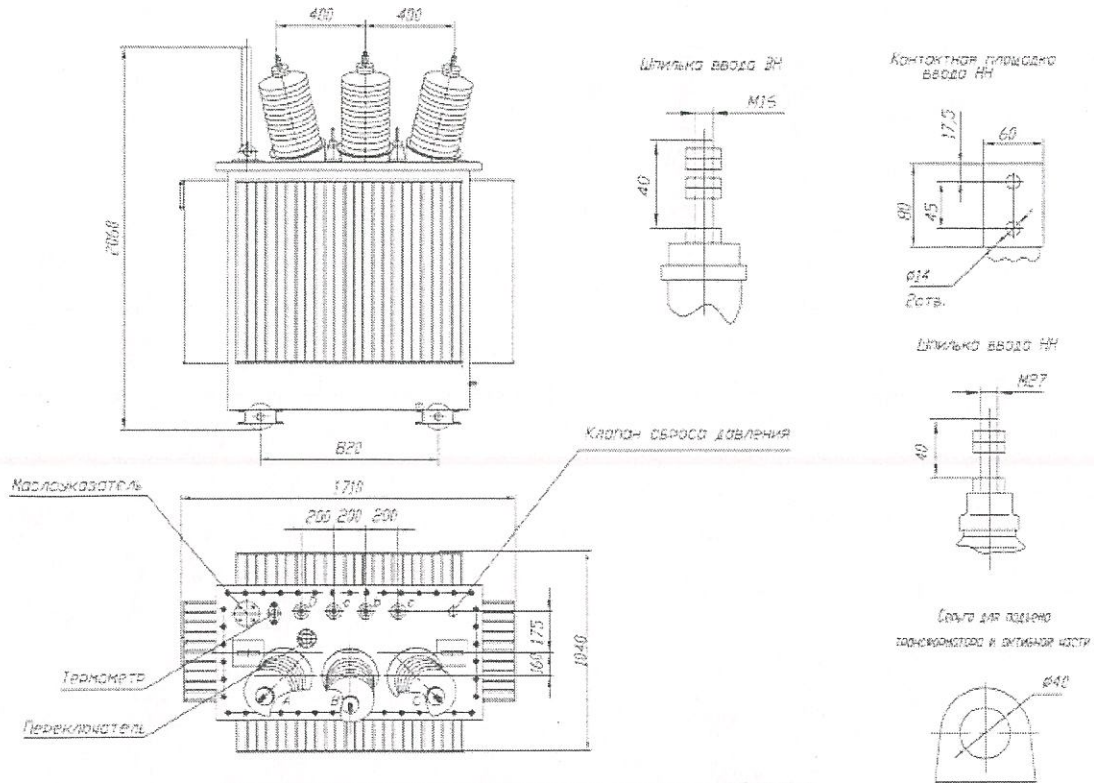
Габаритные, установочные, присоединительные размеры трансформатора ТМ-630/35-01.
